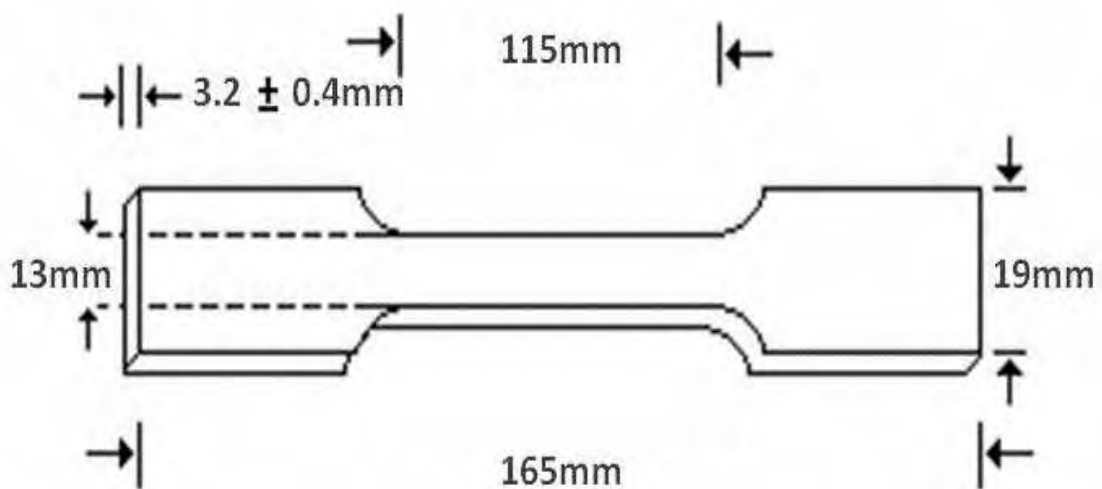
Vista superior e dimensões em mm, do corpo de prova para o ensaio de tração.
